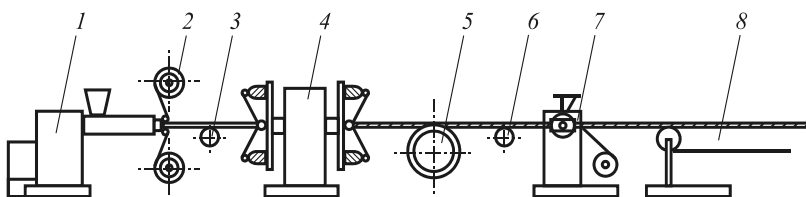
Схема агрегатов для сборки напорных рукавов бездорновым способом без разделением операций:
